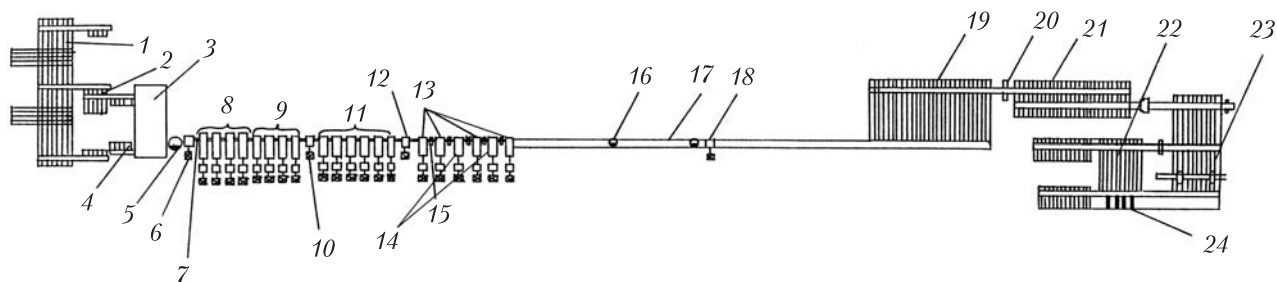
Схема расположения основного технологического оборудования стана 320: 1 – загрузочная решетка; 2 – устройство для загрузки заготовок; 3 – нагревательная печь; 4 – устройство выдачи заготовок (разгрузочный рольганг); 5 – трайб-аппарат; 6 – маятниковые ножницы; 7 – устройство для удаления окалины; 8, 9 – черновая группа клеток; 10 – ротационные ножницы; 11 – промежуточная группа клеток; 12 – ротационные ножницы; 13 – горизонтальные клетки чистовой группы; 14 – вертикальные клетки чистовой группы; 15 – комбинированные петлерегуляторы; 16 – трайб-аппараты; 17 – устройство для охлаждения проката с рольгангом; 18 – ротационные ножницы; 19 – холодильник; 20 – правильная машина; 21 – цепное переключательное устройство с накопителем; 22 – участок пакетирования фасонного проката; 23 – участок пакетирования пруткового проката; 24 – вязальные машины
